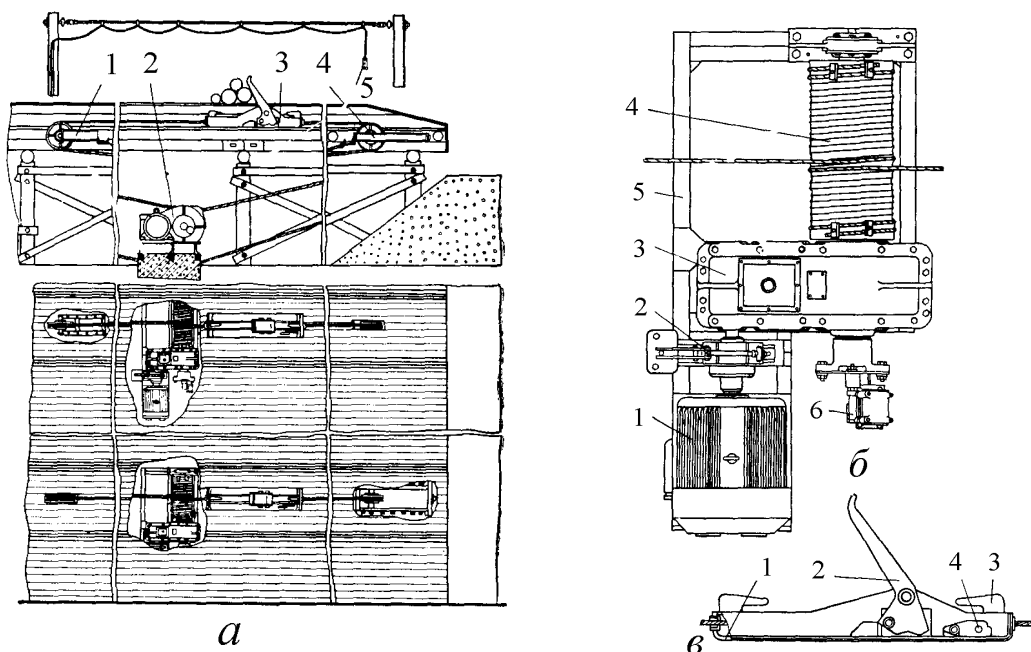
Разгрузочно-растаскивающая установка ЛТ-10: *a* – общий вид установки: 1 – направляющий туер; 2 – лебедка; 3 – челночный захват; 4 – натяжной туер; 5 – пульт управления; *б* – общий вид лебедки: 1 – электродвигатель; 2 – тормоз; 3 – редуктор; 4 – барабан; 5 – рама; 6 – конечный выключатель; *в* – челночный захват:
